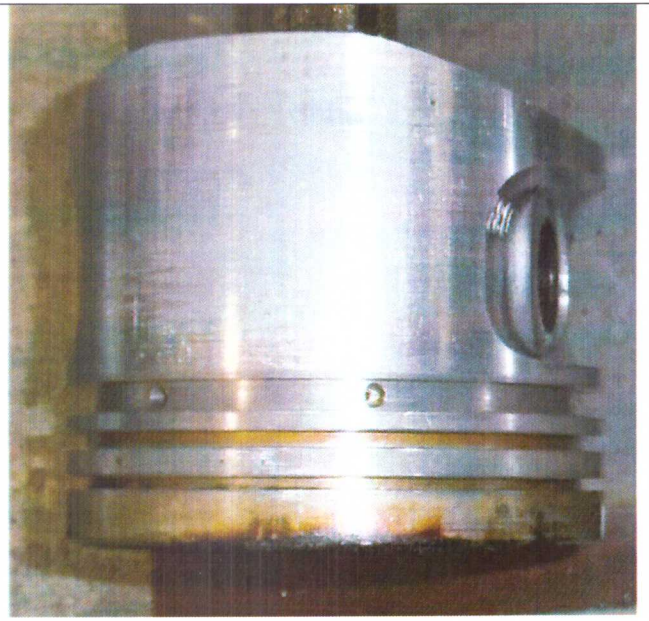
Внешний вид боковой поверхности поршня четвертого цилиндра по окончании длительных испытаний двигателя при работе на базовом масле Castrol EDGE с добавкой нанокompозита Amortect PROOF
